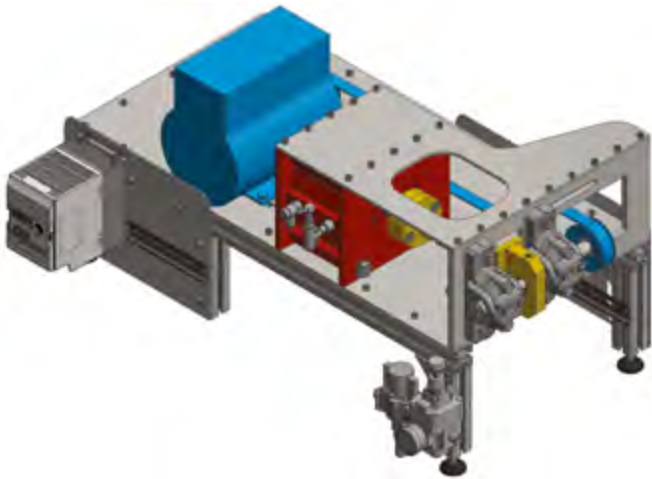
Versuchsaufbau für den beschleunigten Lagerverschleiss, gelb → Halter für Testlager, rot → Erzeugung Lagerbelastung mit einem pneumatischen Zylinder, blau → rotativer Antrieb
